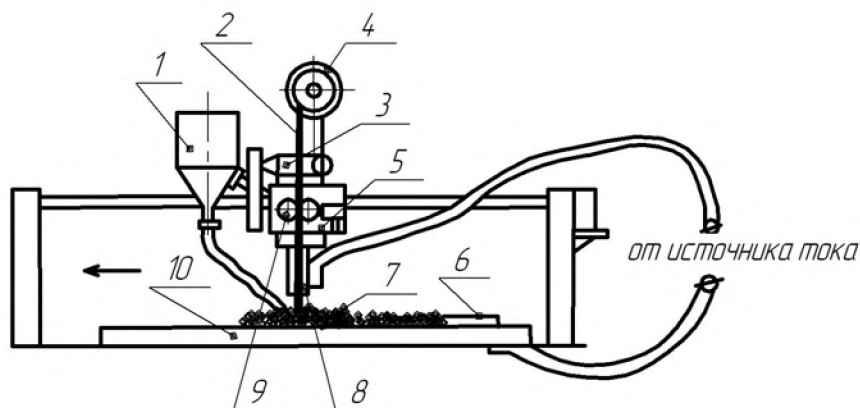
Схема автоматической наплавки под слоем флюса:
